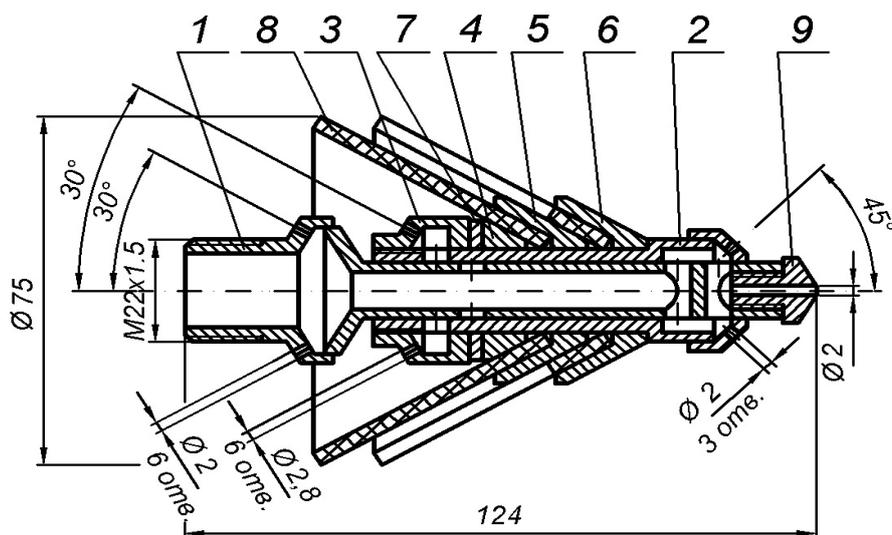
Конструкция реверсивной насадки промывочной мягкой РНПМ-80:
